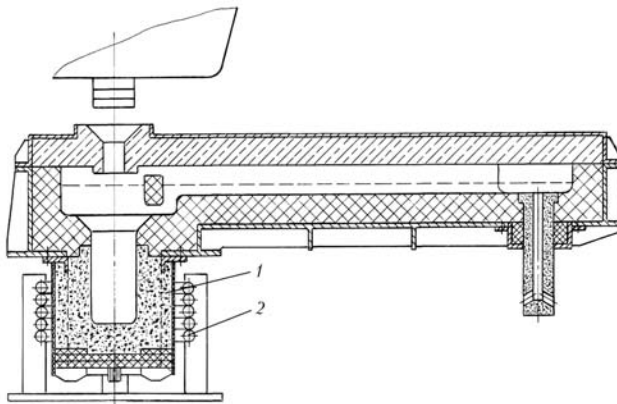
Схема индукционного нагрева в промежуточном ковше: 1 — нагревательный узел; 2 — индуктор
